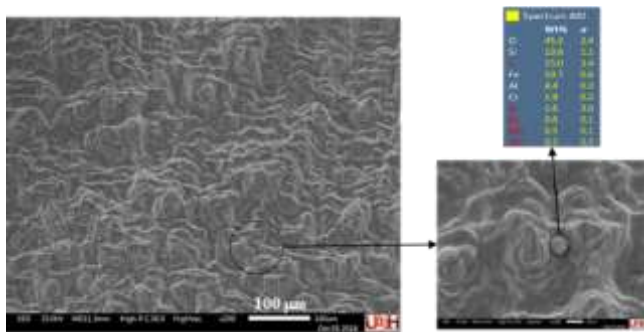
Fractografía del cordón de soldadura en el punto de sujeción.
